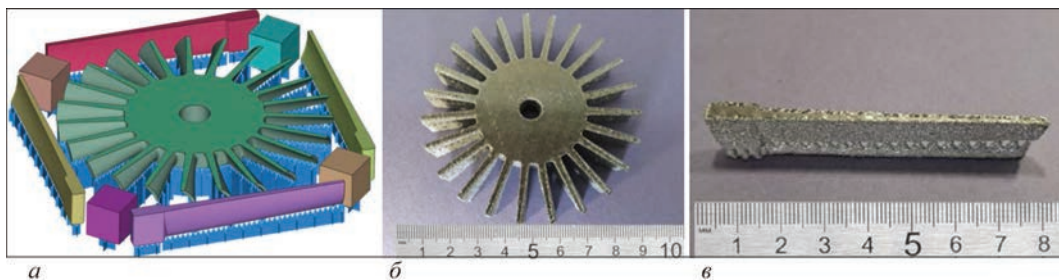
Модель і вироби: а — збірка виробів; б — колесо турбіни; в — лопатка ГТД
